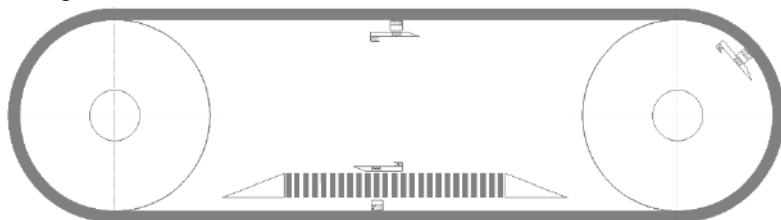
Магнитный ленточный ускоритель с обратной конструкцией.
